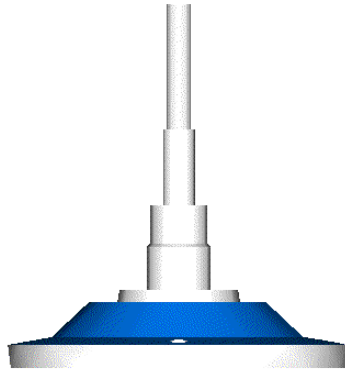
Plato del disco con flecha modificada para acoplamiento de motor impulsor.
